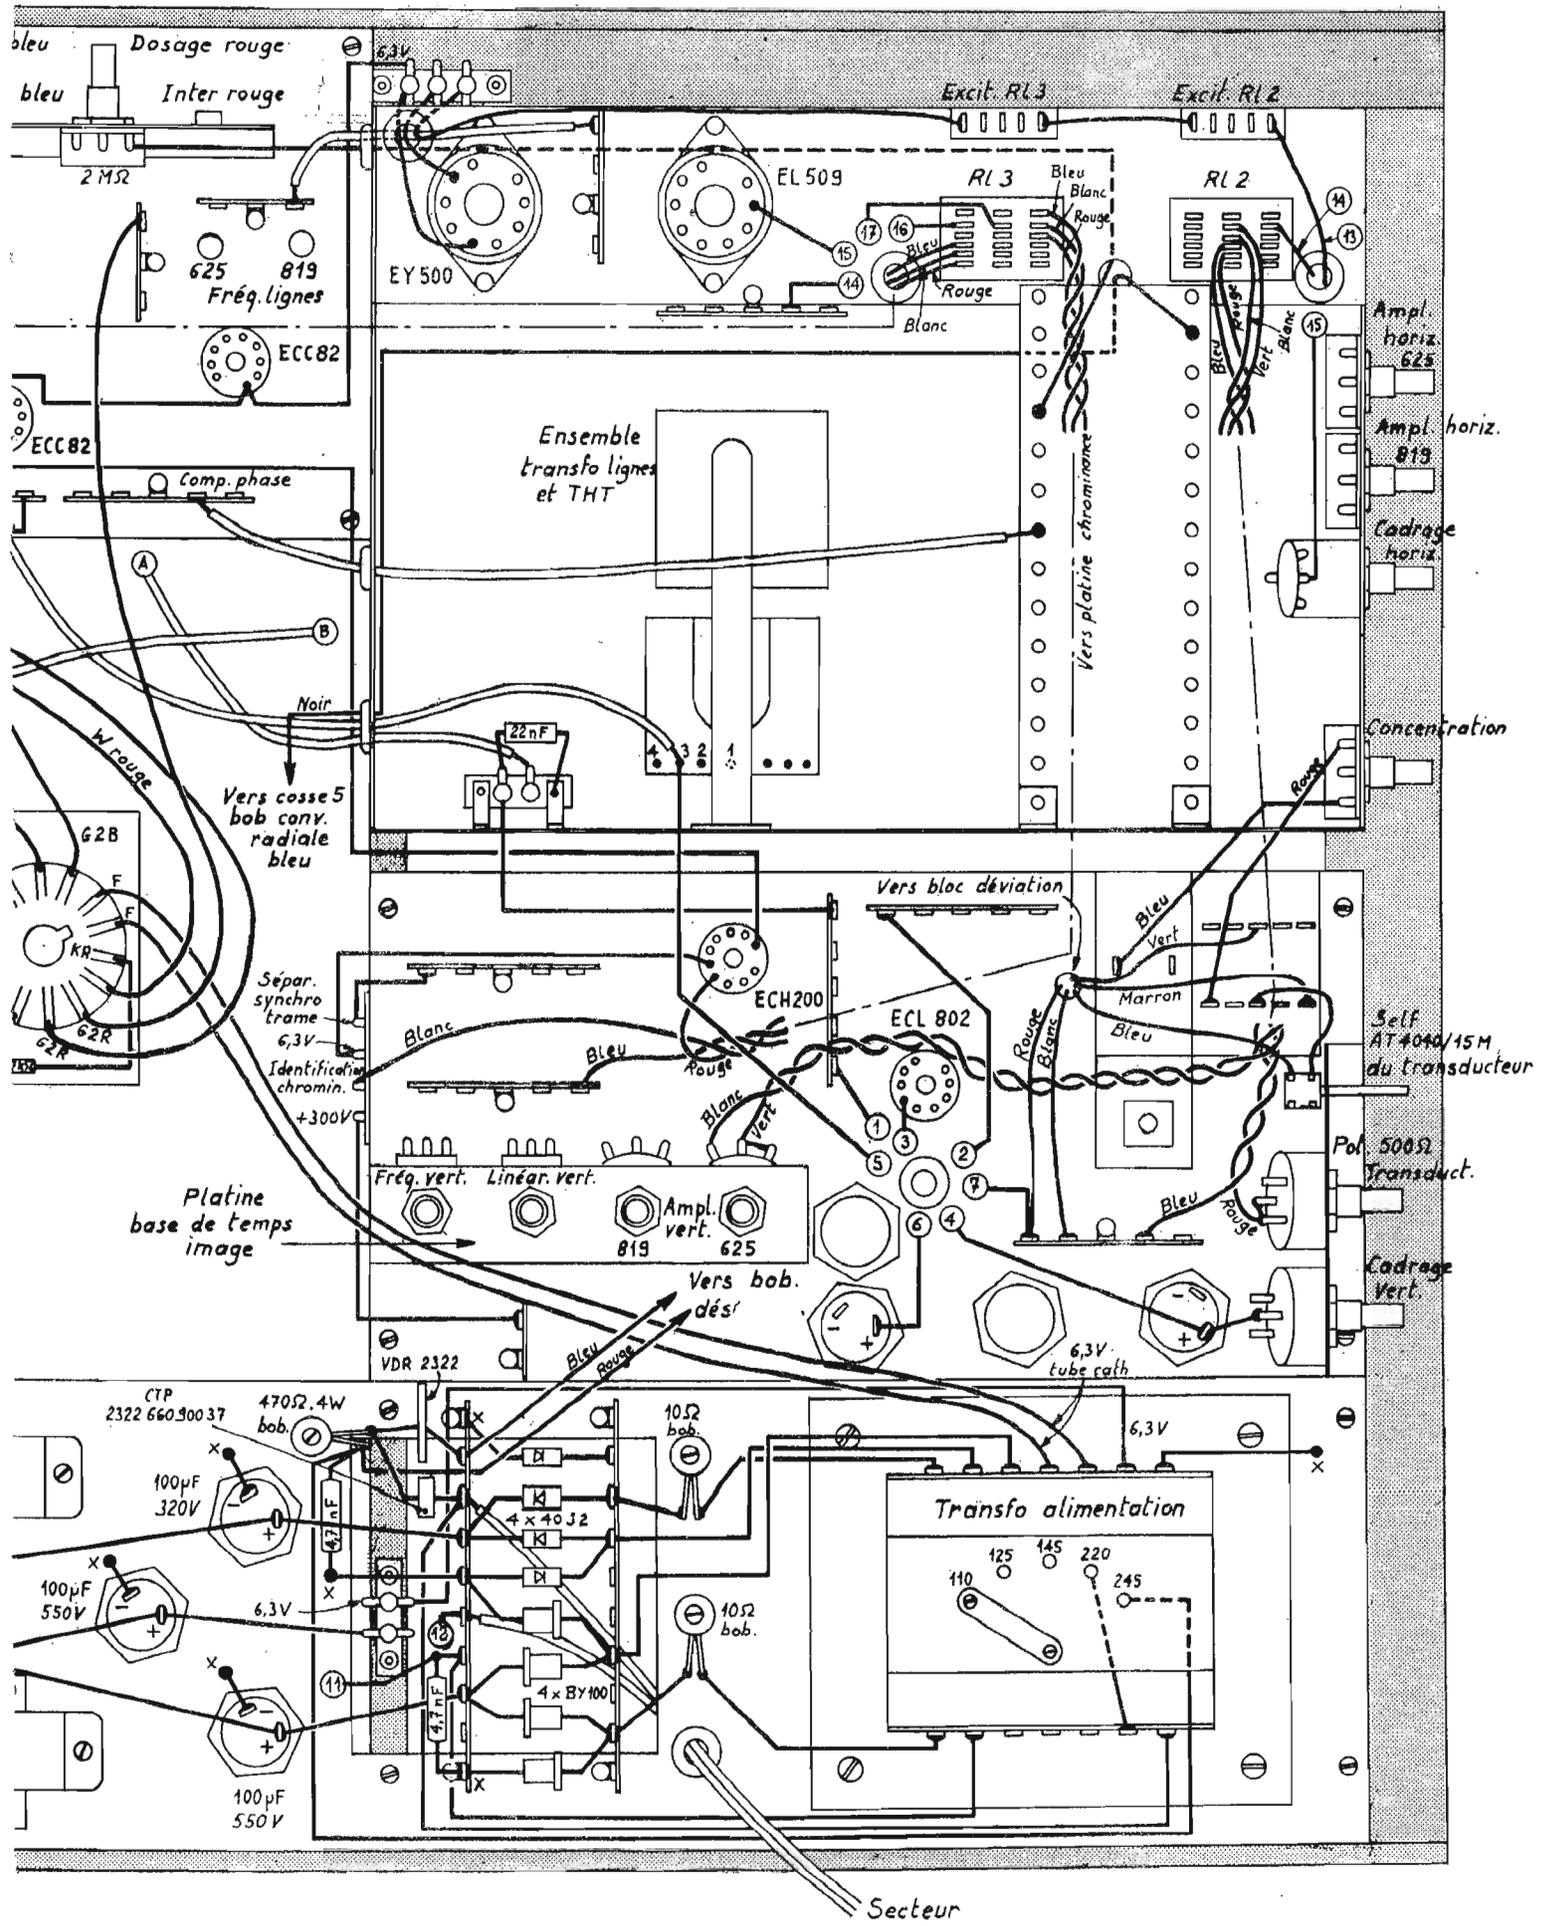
Disposition des sous-ensembles montés sur le châssis
